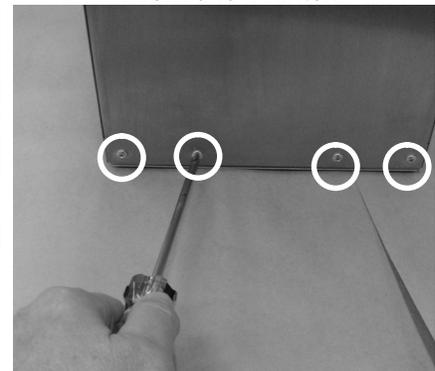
Entfernen des Gebläsesteckers und der Schrauben
